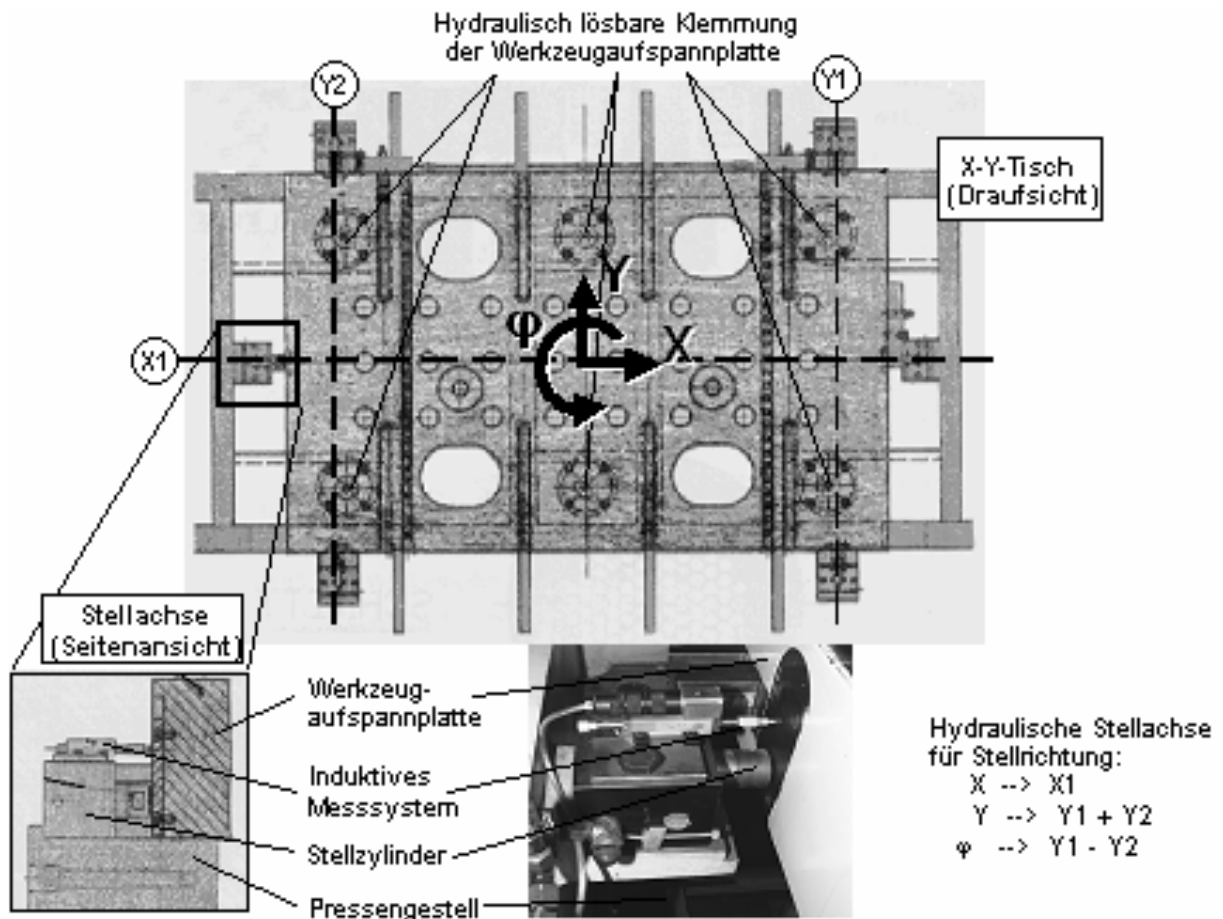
X-Y-lageregelbare Werkzeugaufspannplatte
